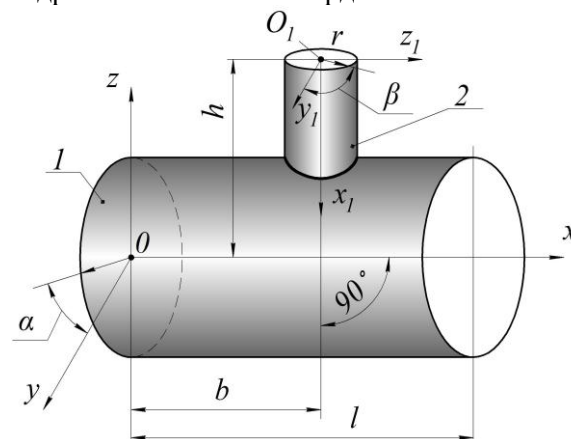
Схема пересечения двух цилиндрических поверхностей: поверхности корпуса 1 и поверхности штуцера 2
